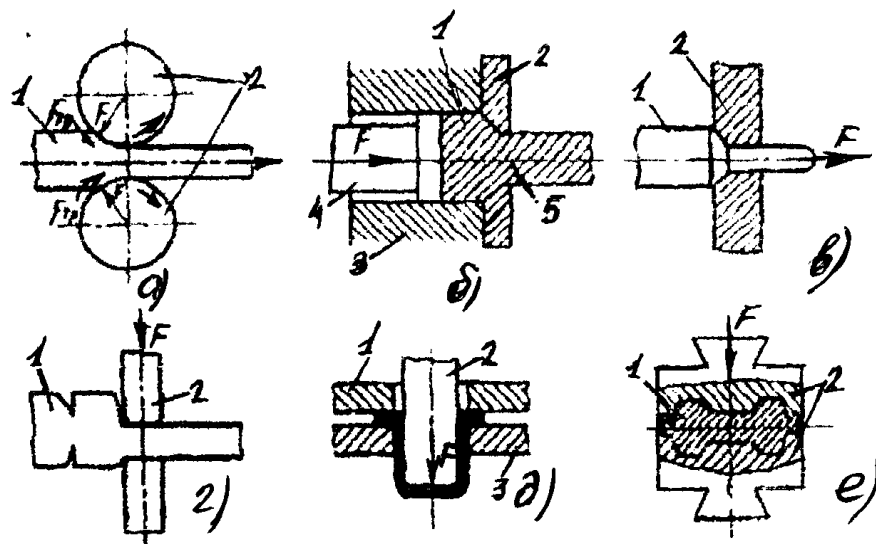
Схеми основних способів обробки металів тиском:
